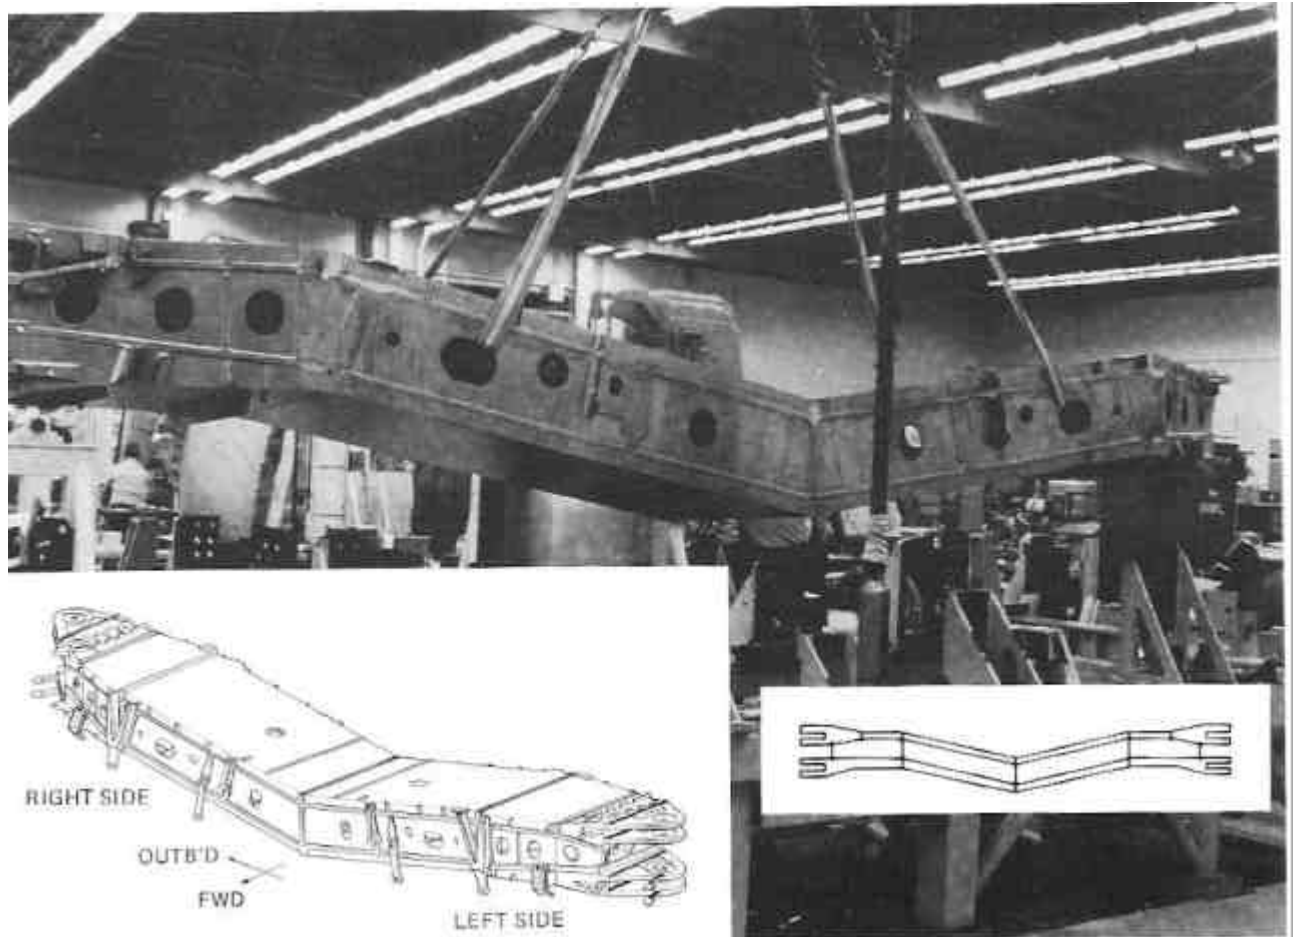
Pianetto centrale dell'ala dell'F-14.
